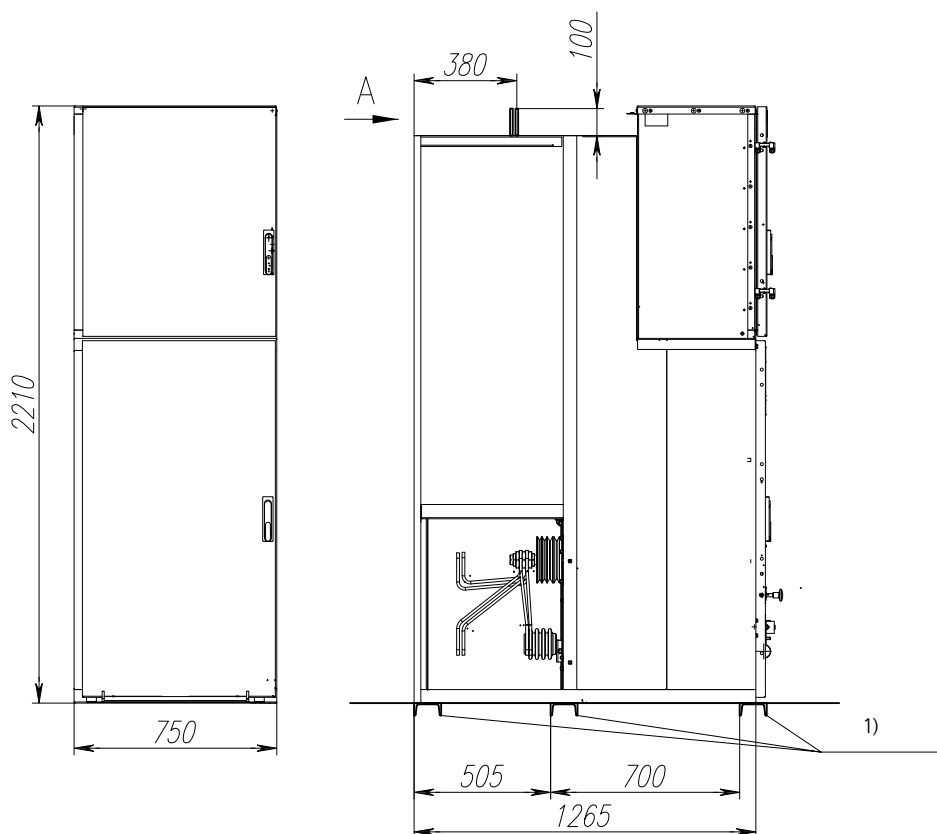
Общий вид и габаритные размеры шкафа К-128 шинного ввода на номинальные токи до 1600 А
